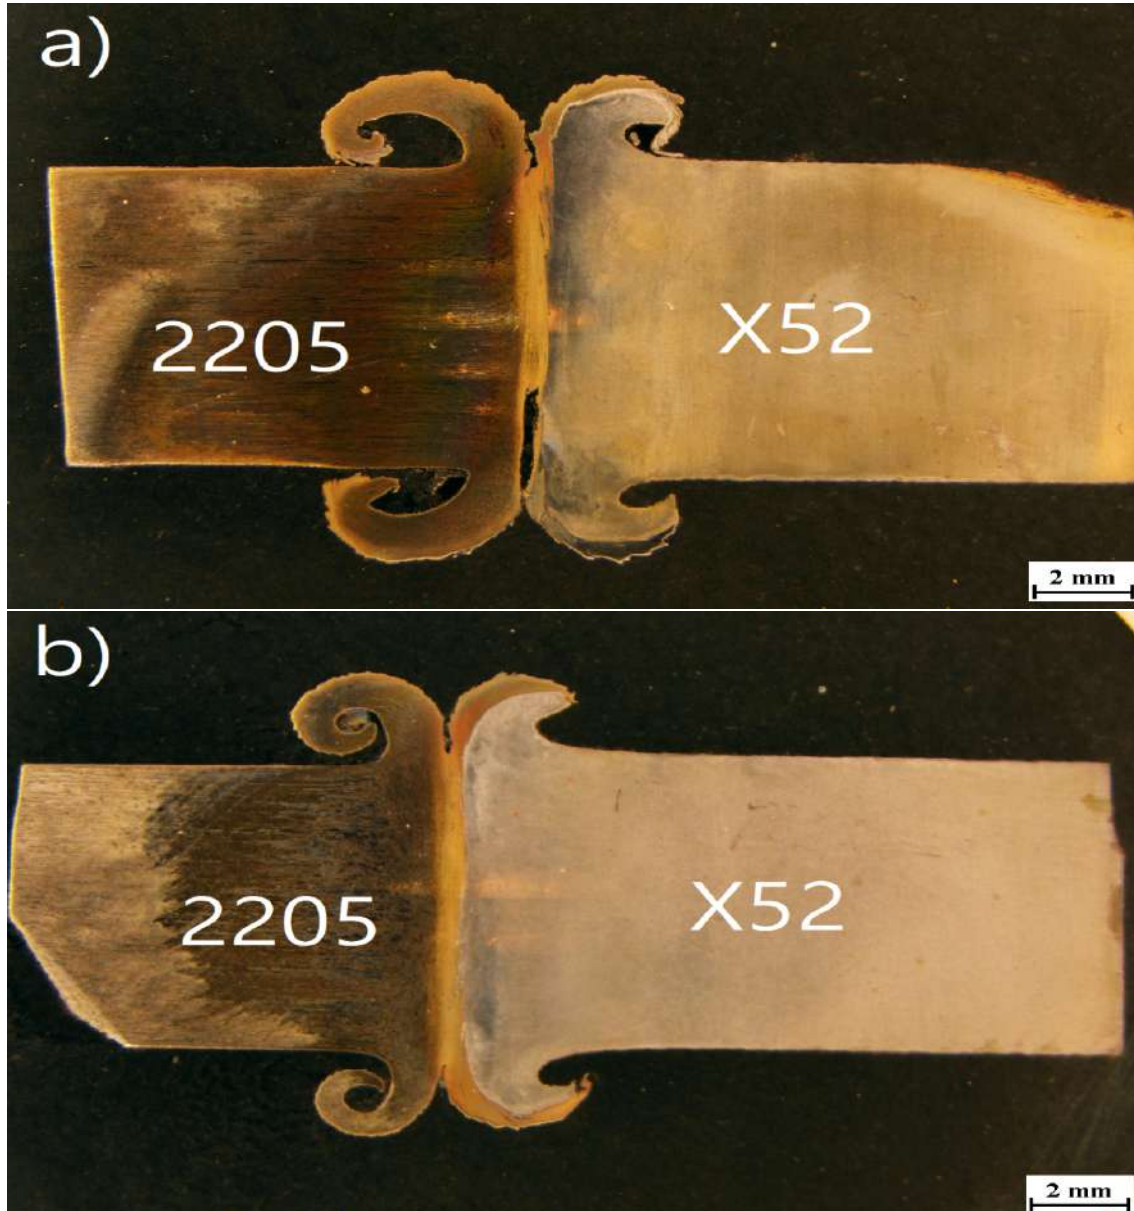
Macrographie des joints soudés, a) Joint optimal, b) joint déficient
